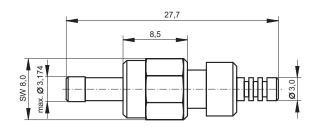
F-SMA Steckverbinder mit 6-Kant Mutter
